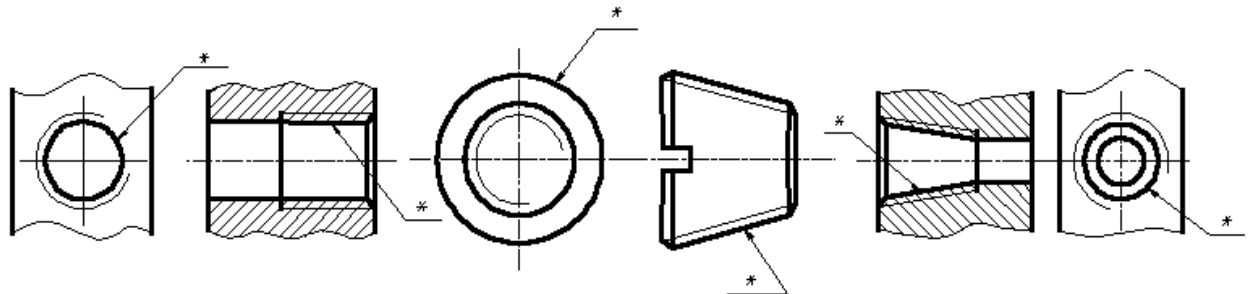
13– Обозначение трубной цилиндрической и конической резьбы
